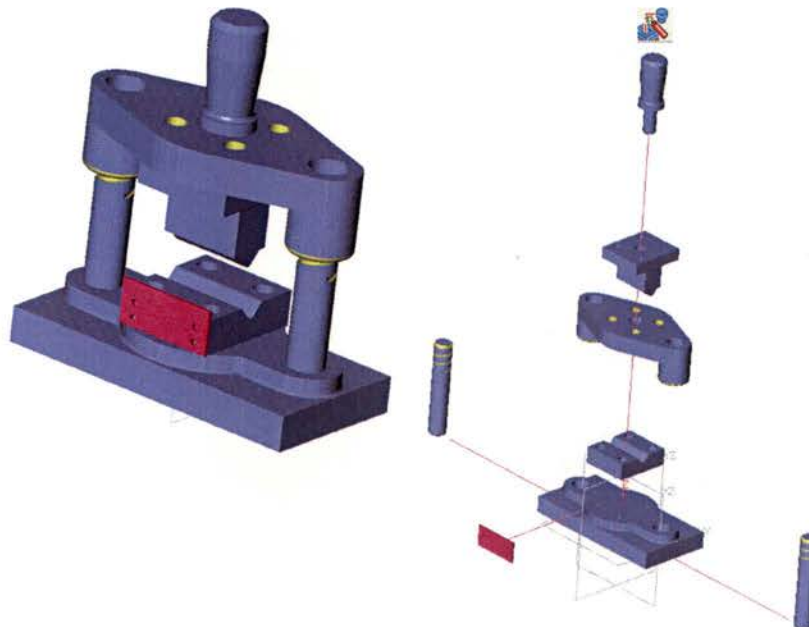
Conjunto final com elementos montados e vista explodida dos vários componentes
